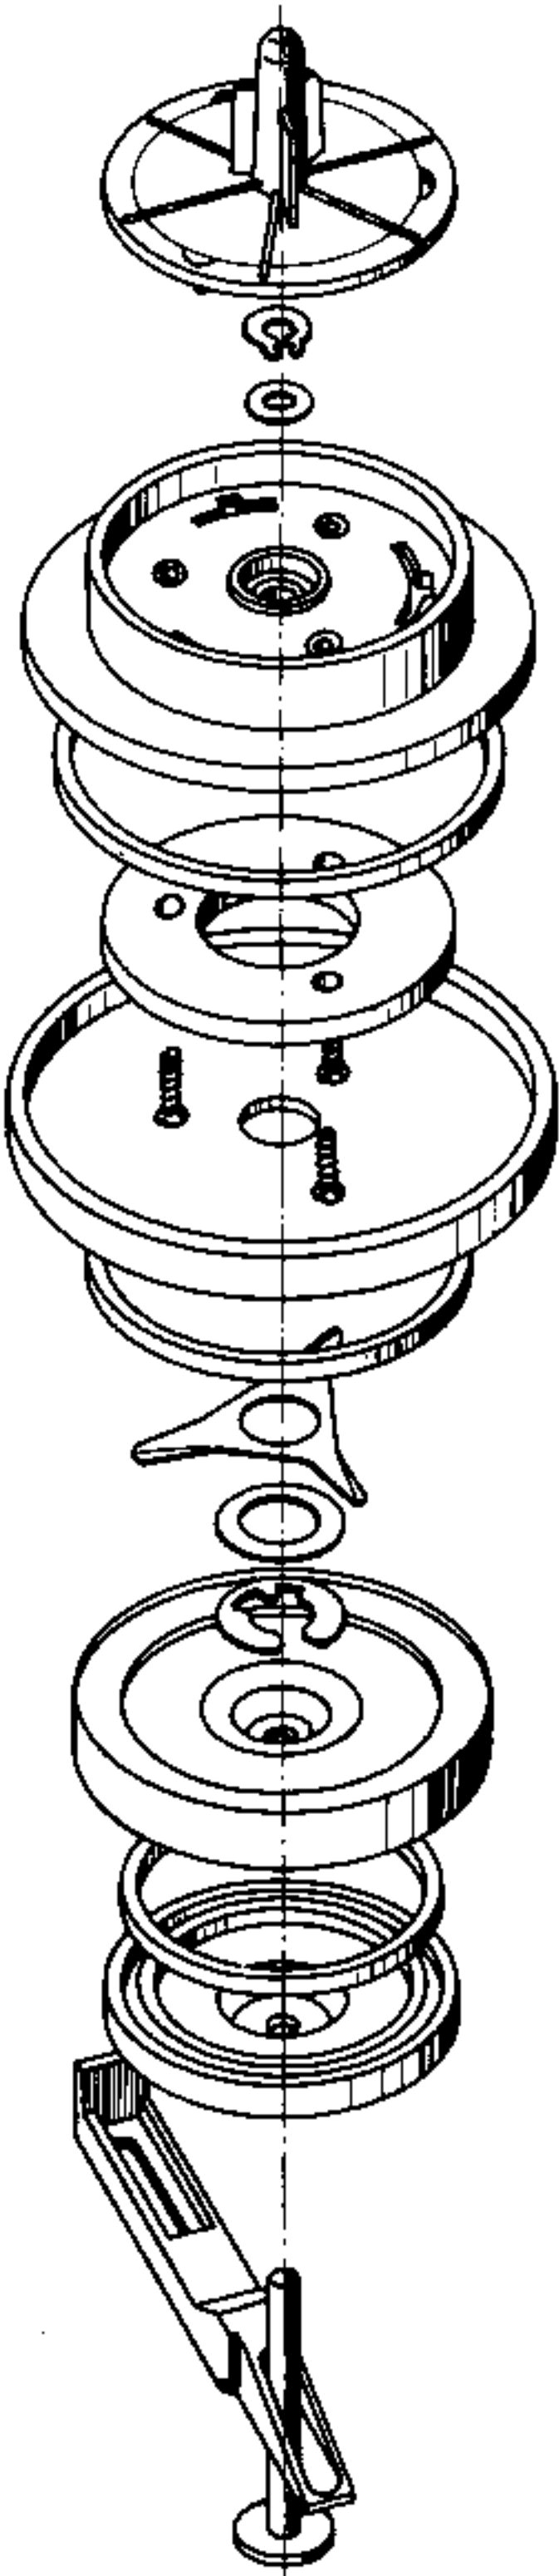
Explodierte Darstellung des rechten Wickeltellers
